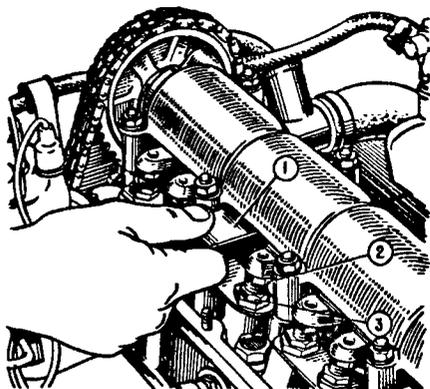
Проверка зазора между рычагами и кулачками распределительного вала: 1 - шуп А.95111; 2 - регулировочный болт; 3 - контргайка регулировочного болта
